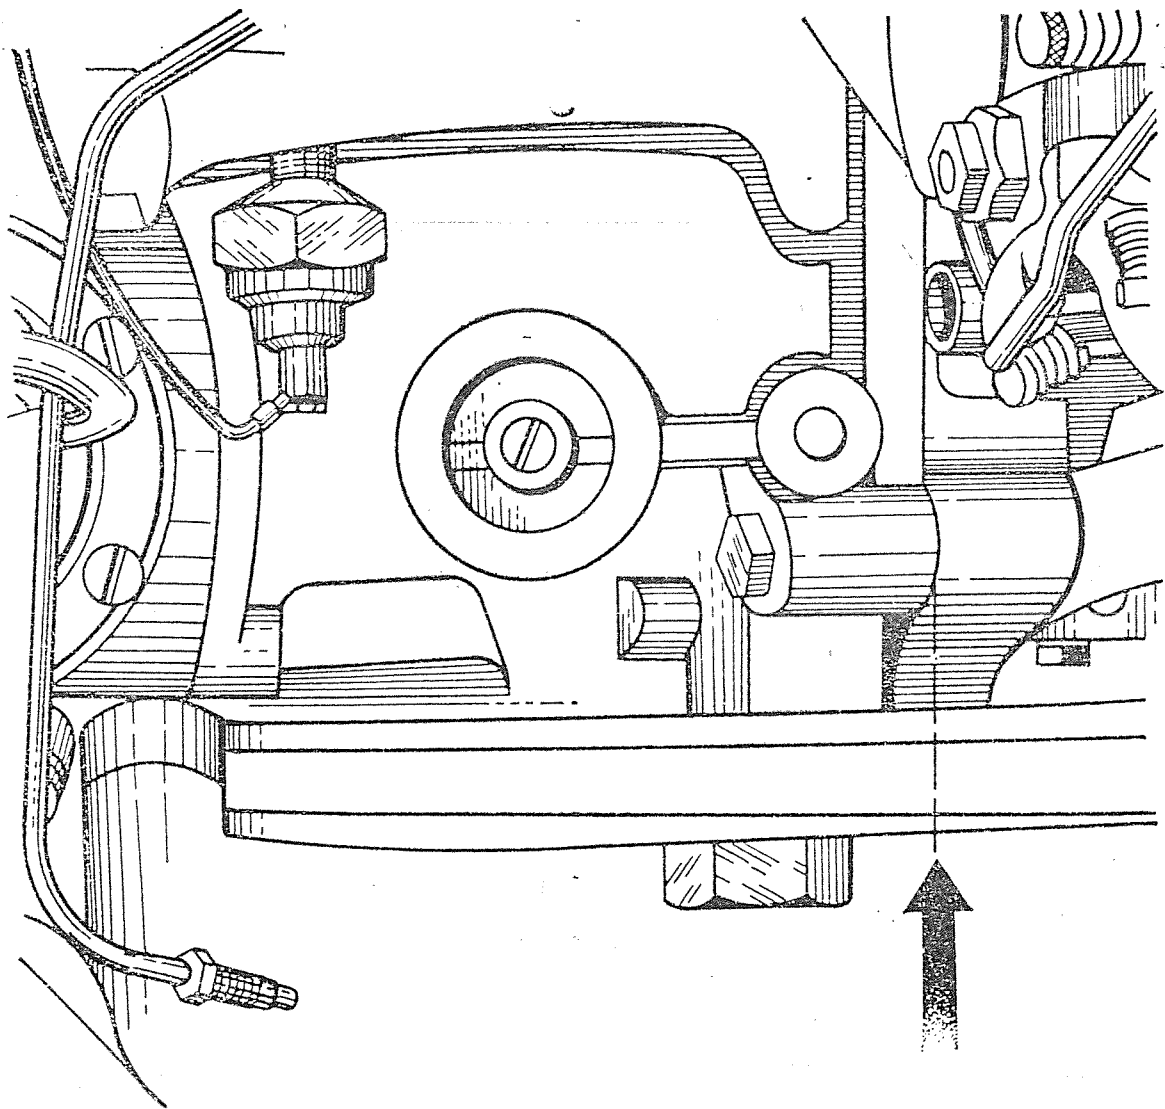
Cuando se instale el eje del distribuidor, debe cuidarse de que el corte desplazado para encastrar en el medio del acoplamiento del distribuidor, quede perpendicular al eje longitudinal del motor (representado por la dirección de la flecha).
